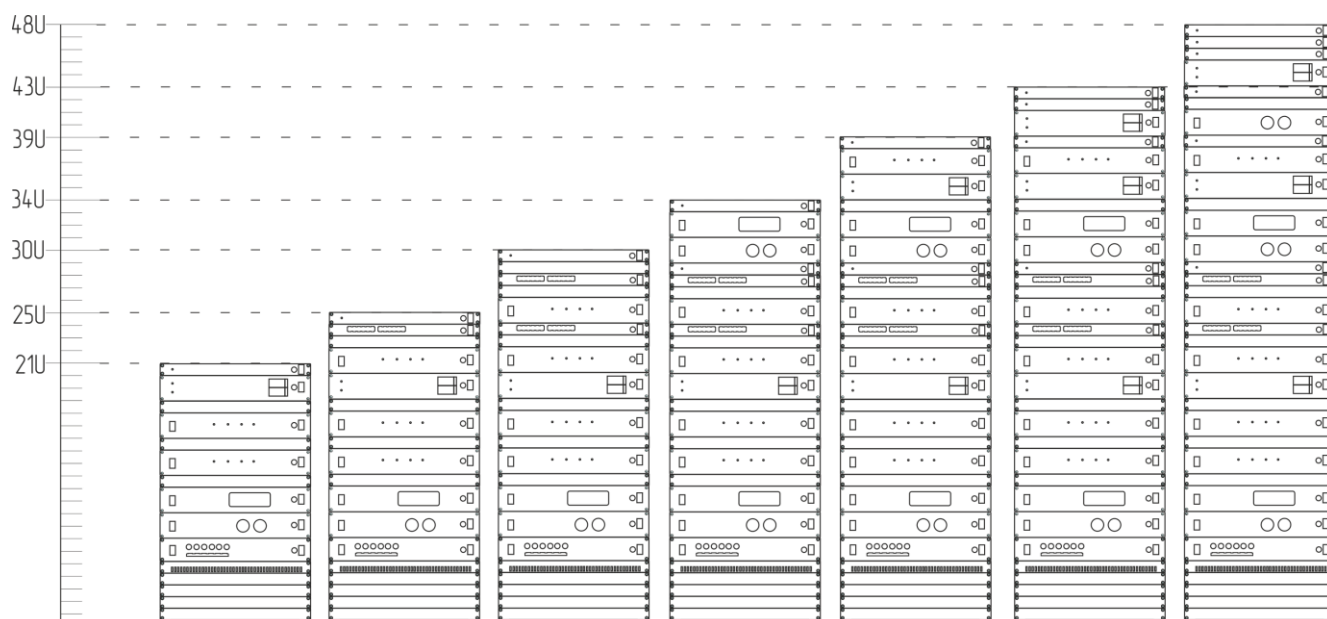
Конструктивный ряд стойки типа 19TKST
